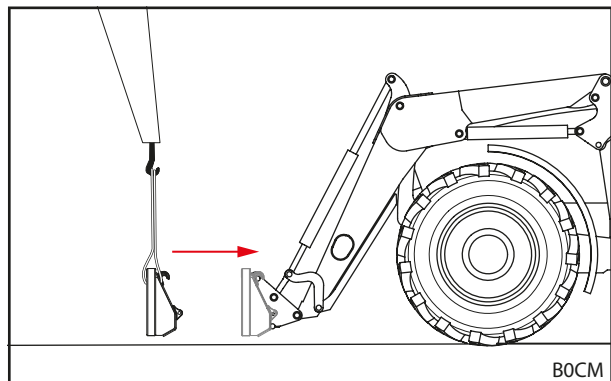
Accrocher le cadre dans le cadre porte-outils
